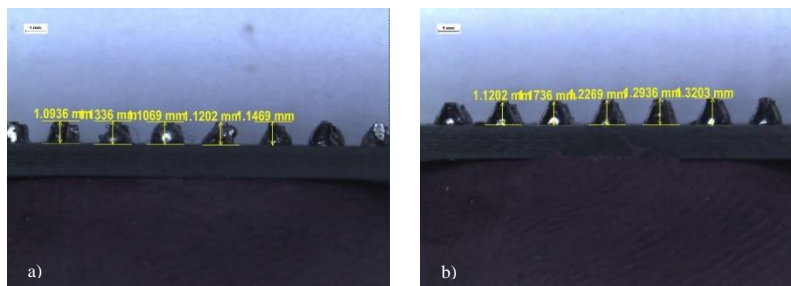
Medición de tamaños de soldadura a) muestra 1 y b) muestra 2.
